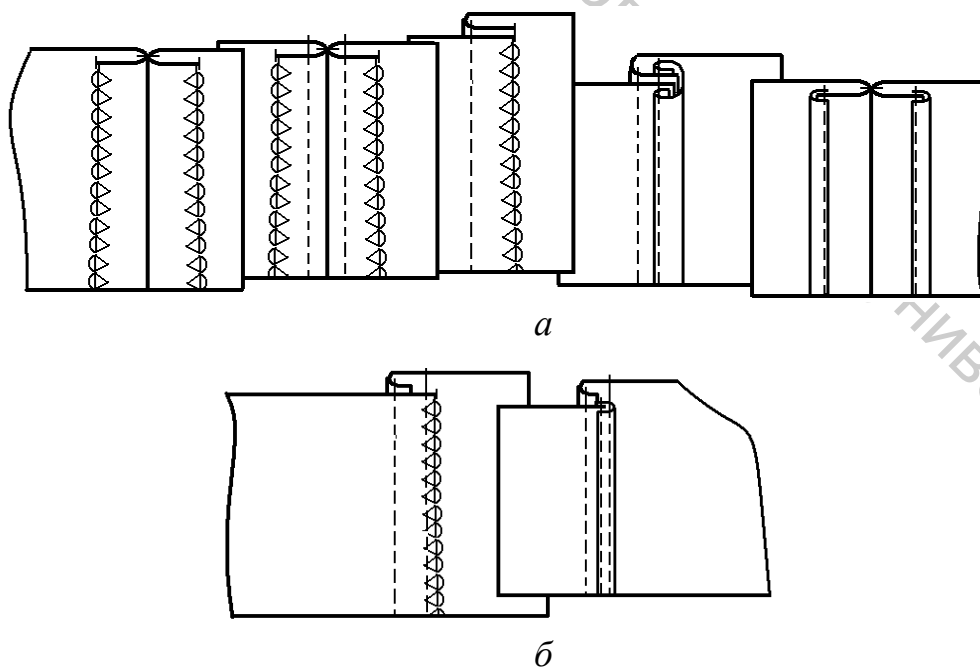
Соединение деталей однослойной пристегивающейся подкладки
